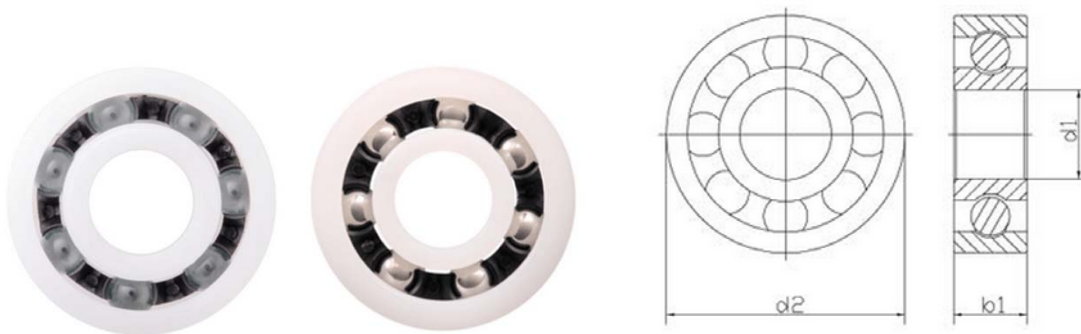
Rodamientos de bolas Xiros B180. Fuente: www.igus.com
